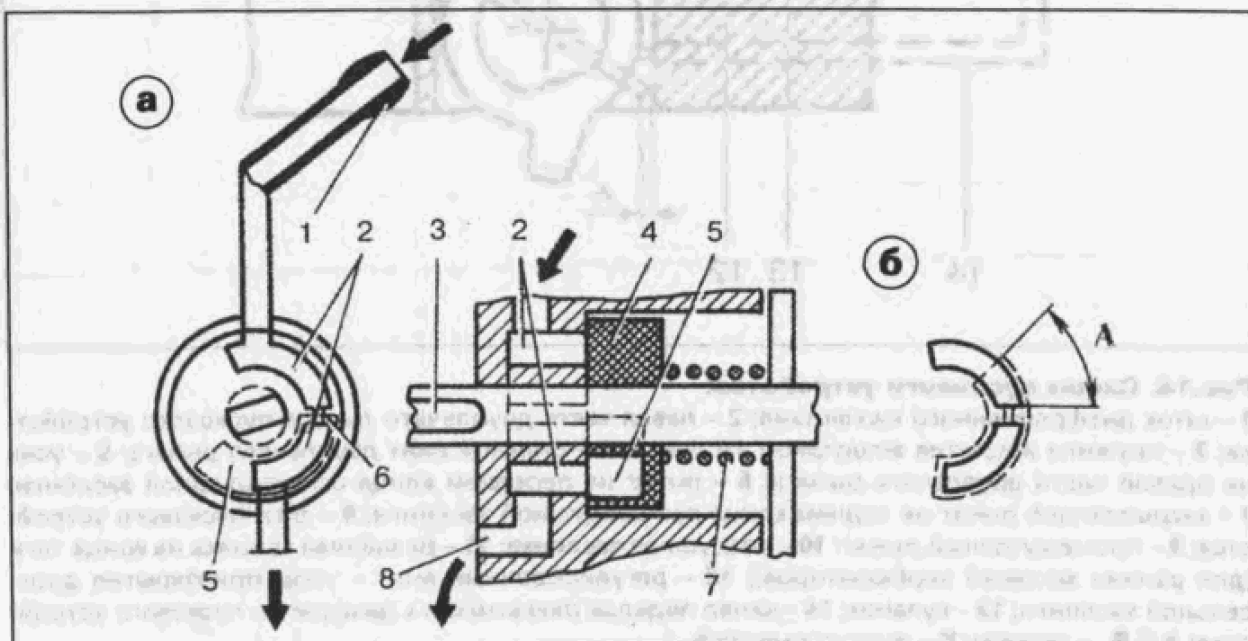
Регулирующее устройство вентиляции картера: а – конструкция; б – перекрытие кромок выемок при повороте золотника:
